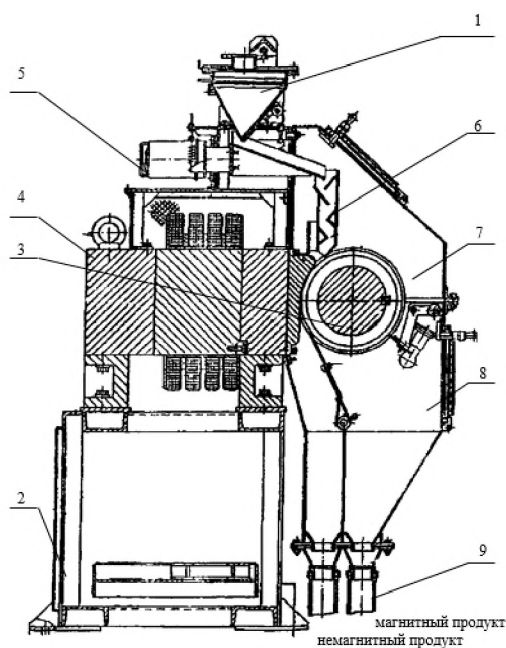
Электромагнитный валковый сепаратор 272-СЭ: 1 - бункер; 2 - рама; 3 - валок; 4 - электромагнитная система; 5 - питатель, 6 - проба; 7 - кожух; 8 - ванна; 9 – сборник.
